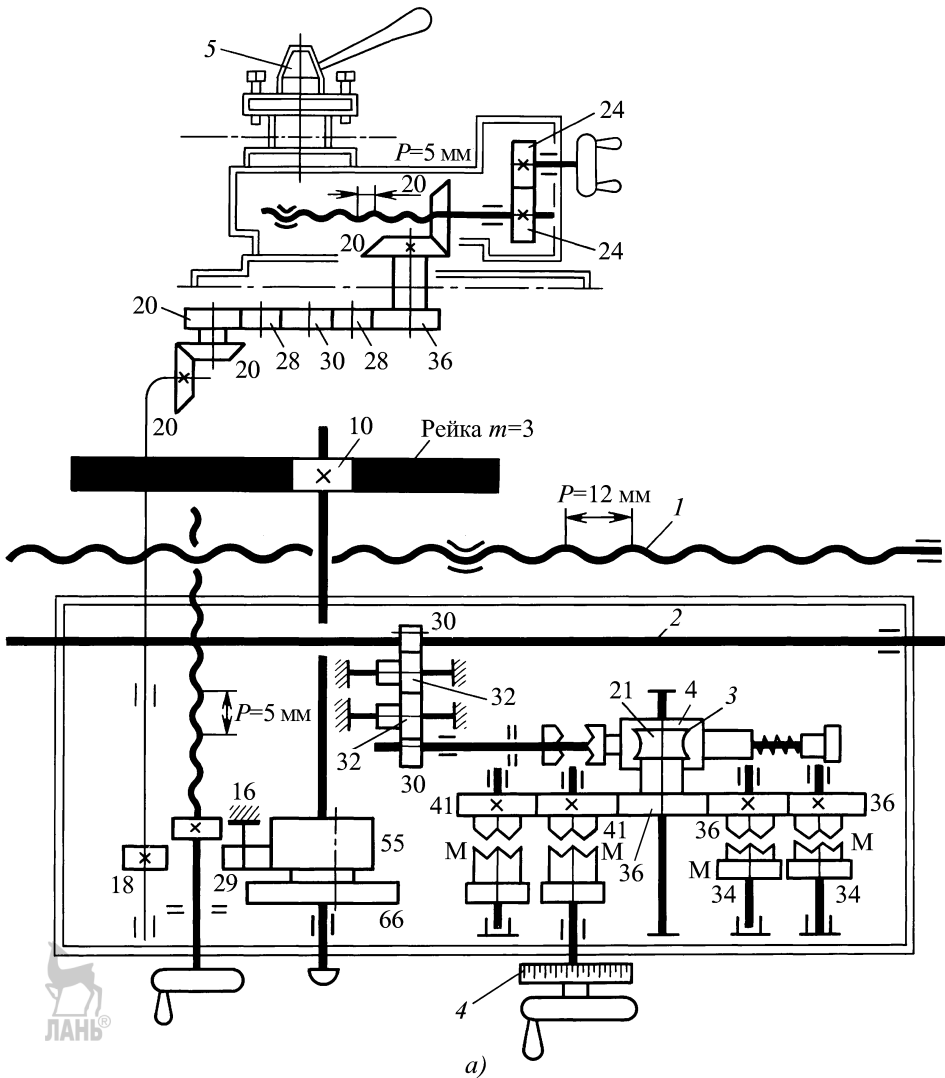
Кинематическая схема фартука и верхних салазок токарно-винторезных станков 16К20П (а) и верхних салазок 1М163 (б) (начало):
